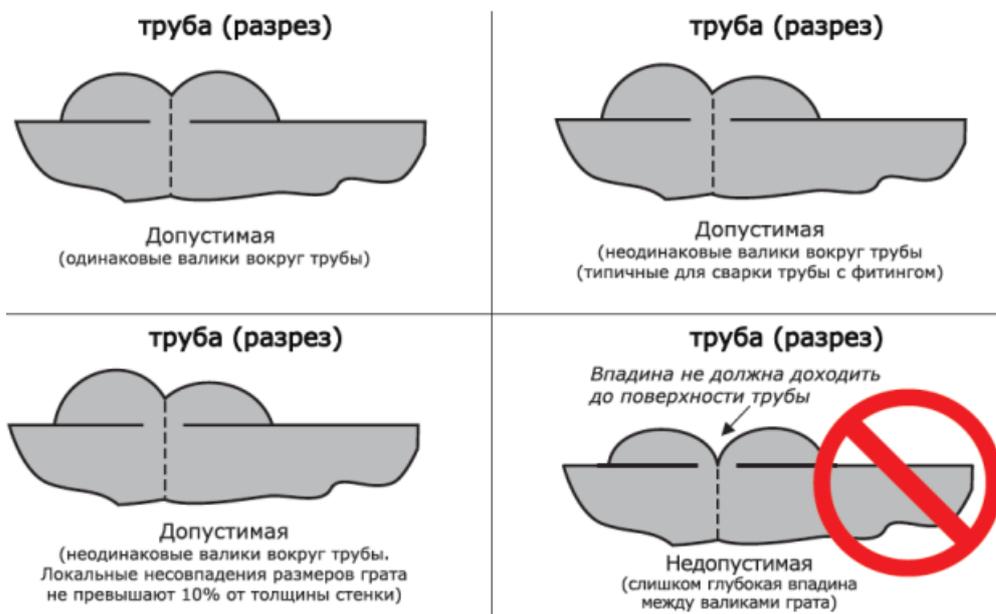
Вид грата при сварке нагретым инструментом
